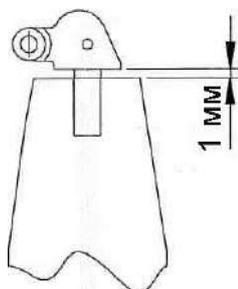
Регулировка лабиринтного уплотнения
